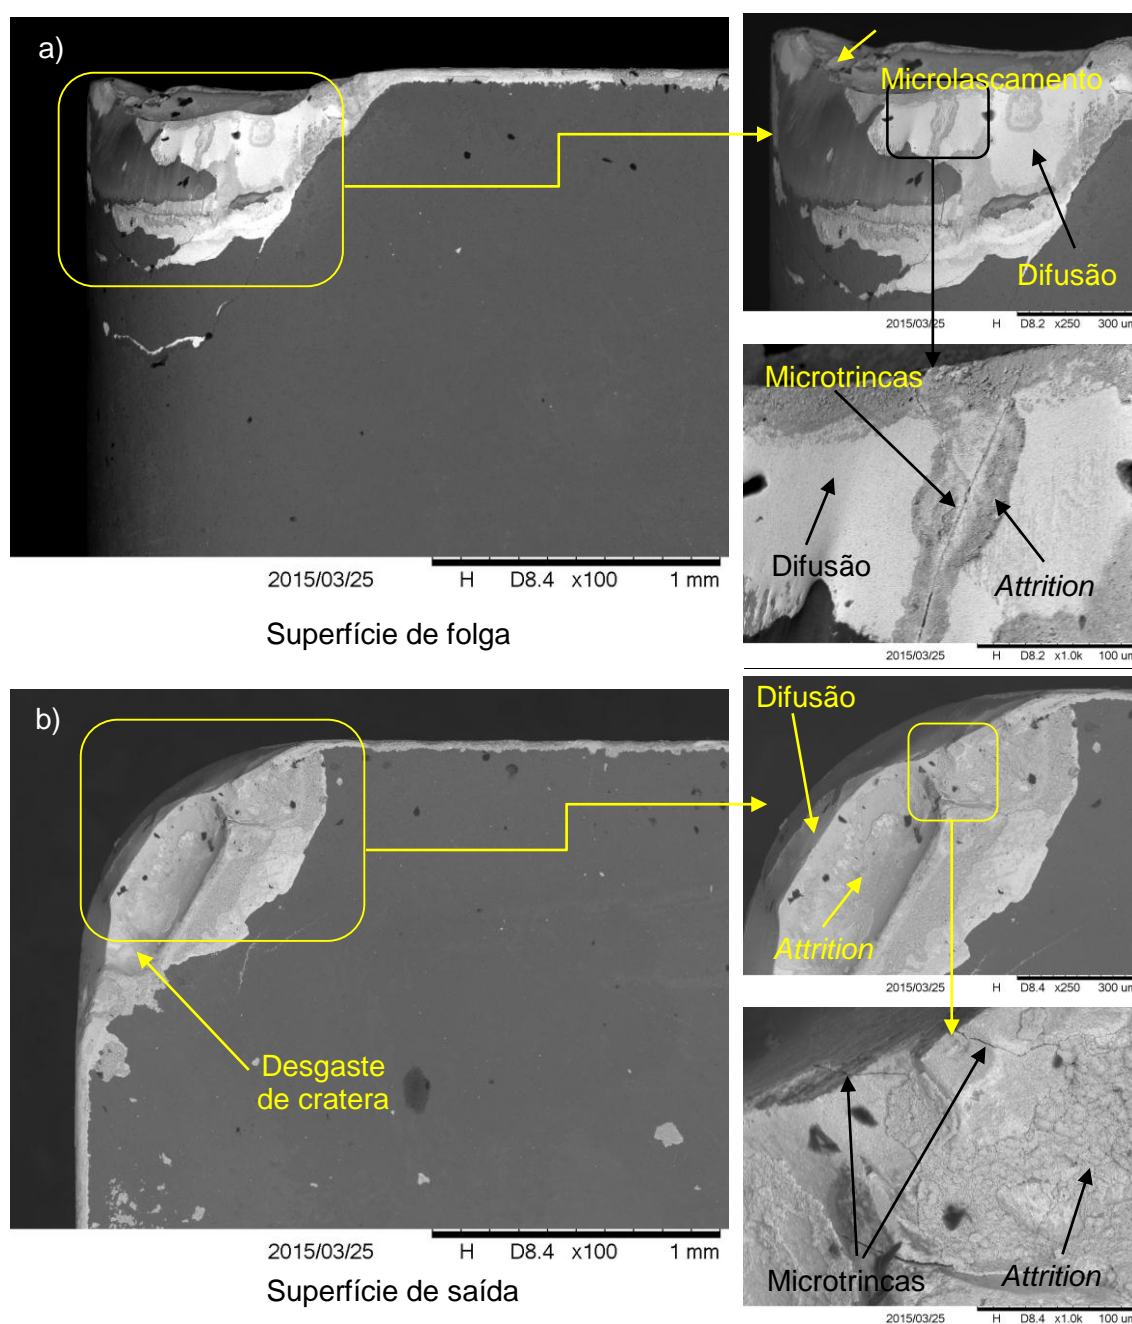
Fotos obtidas através do MEV das ferramentas de metal duro após a usinagem do Inconel 718 com aplicação de fluido de corte Vasco 1000 + 5% de grafite por jorro. (a) superfície de folga e (b) superfície de saída. Velocidade de corte 50 m/min, avanço 0,1 mm/rot e profundidade de corte de 0,5 mm.
